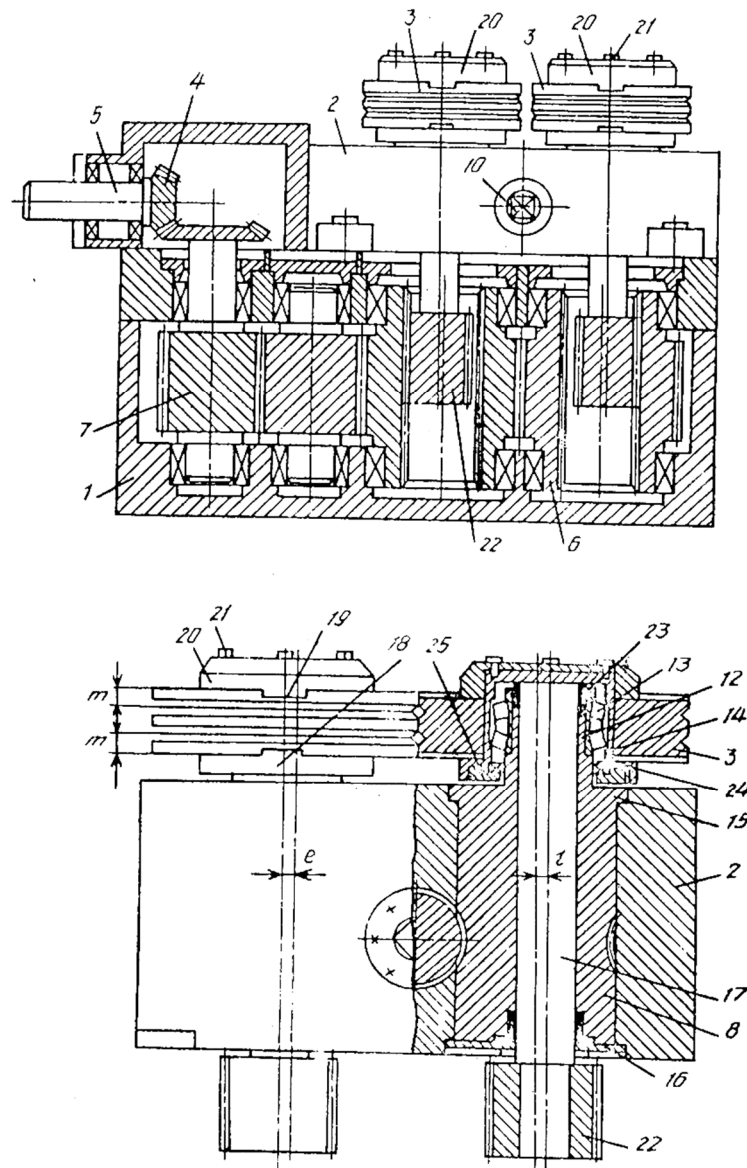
Установка валкової касети на редукторі, розріз по осі редуктора і валкова касета в зборі, вид збоку
